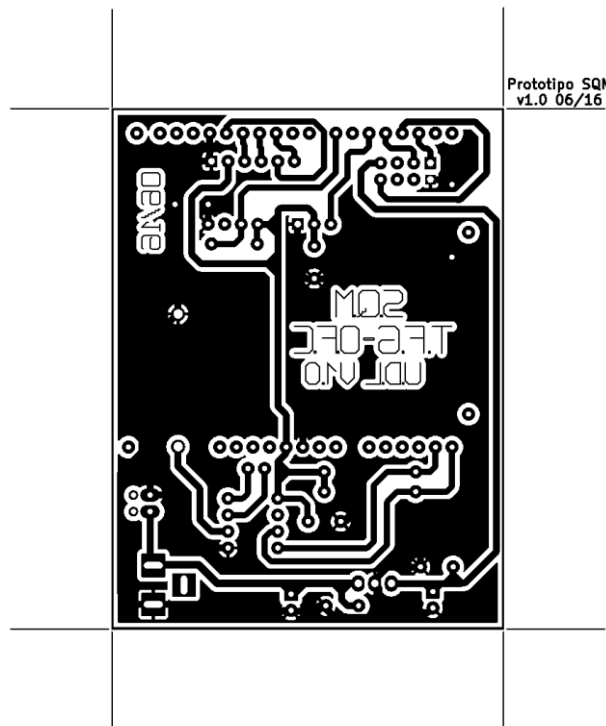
Plantilla del PCB llesta per imprimir sobre la placa de fibra de vidre
